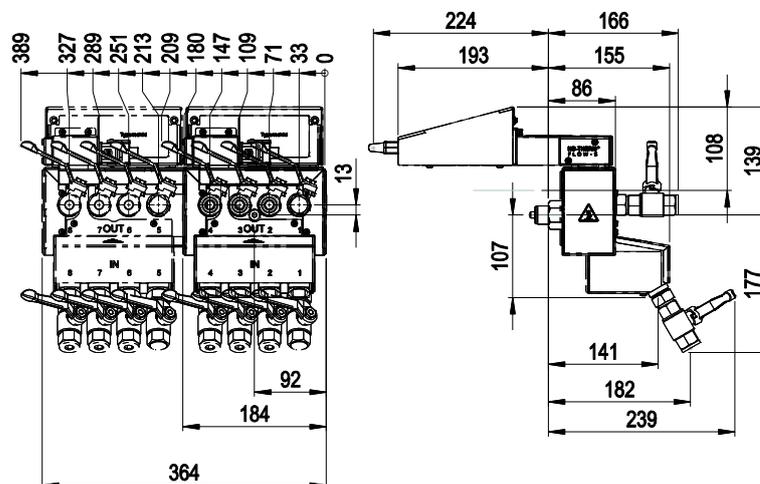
Размеры конструкции: навесной прибор Thermo-5
